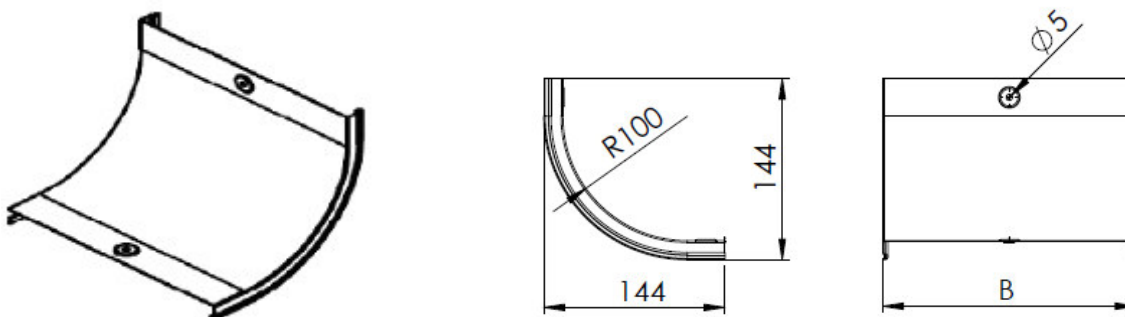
Крышка CS 90 на угол вертикальный внутренний 90°
